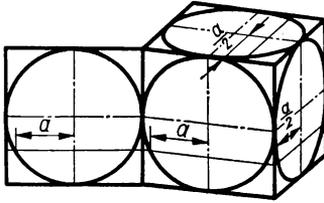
Zeichnen der Ellipse mit Hilfskonstruktion, erstes Verfahren
